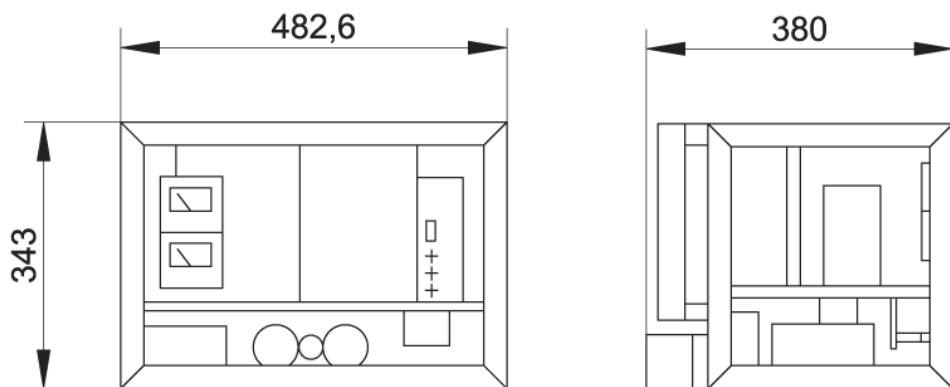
(а). Габаритный чертеж конвертора КУВ-2 (двухместный каркас)
